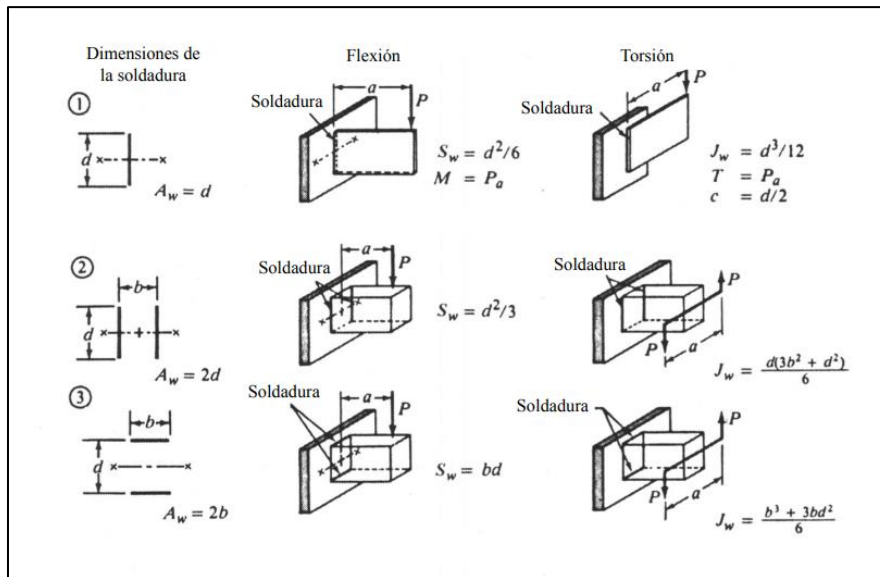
Factores geométricos para analizar la soldadura como una línea
